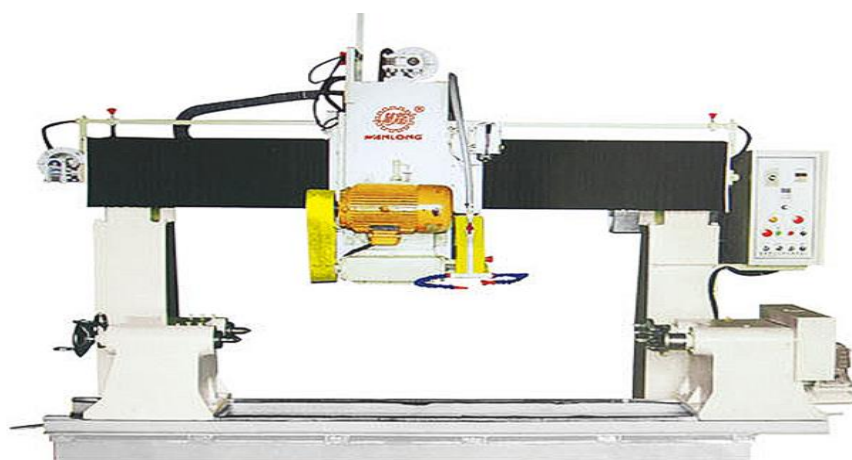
Верстат для поверхневої обробки каменю YFQ-290/700
